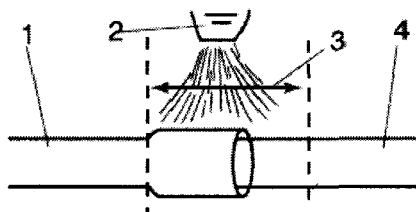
Размещение горелки при пайке труб: 1 — наружная труба; 2 — горелка; 3 — зона нагрева; 4 — внутренняя труба
